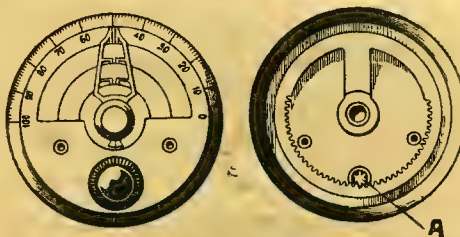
Наружный и внутренний вид ручки верньера с двумя зубчатками. Направо видно колесо с большим вырезом и внутренней зубчатой нарезкой.
